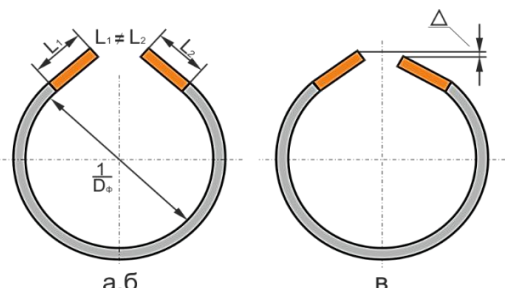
Дефекты трубной заготовки при вальцовой формовке:
